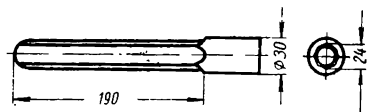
Размеры заготовки (к примеру расчета ромбического ручья)
